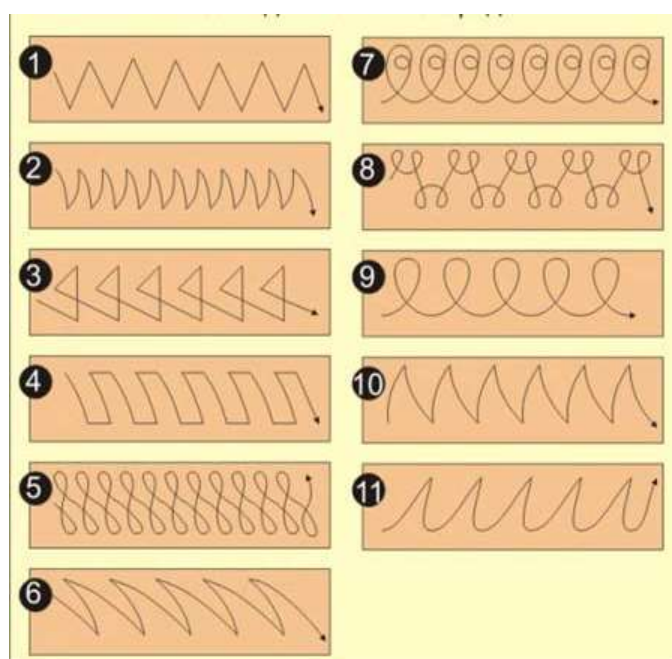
Схемы движения электрода при ручной дуговой сварке
